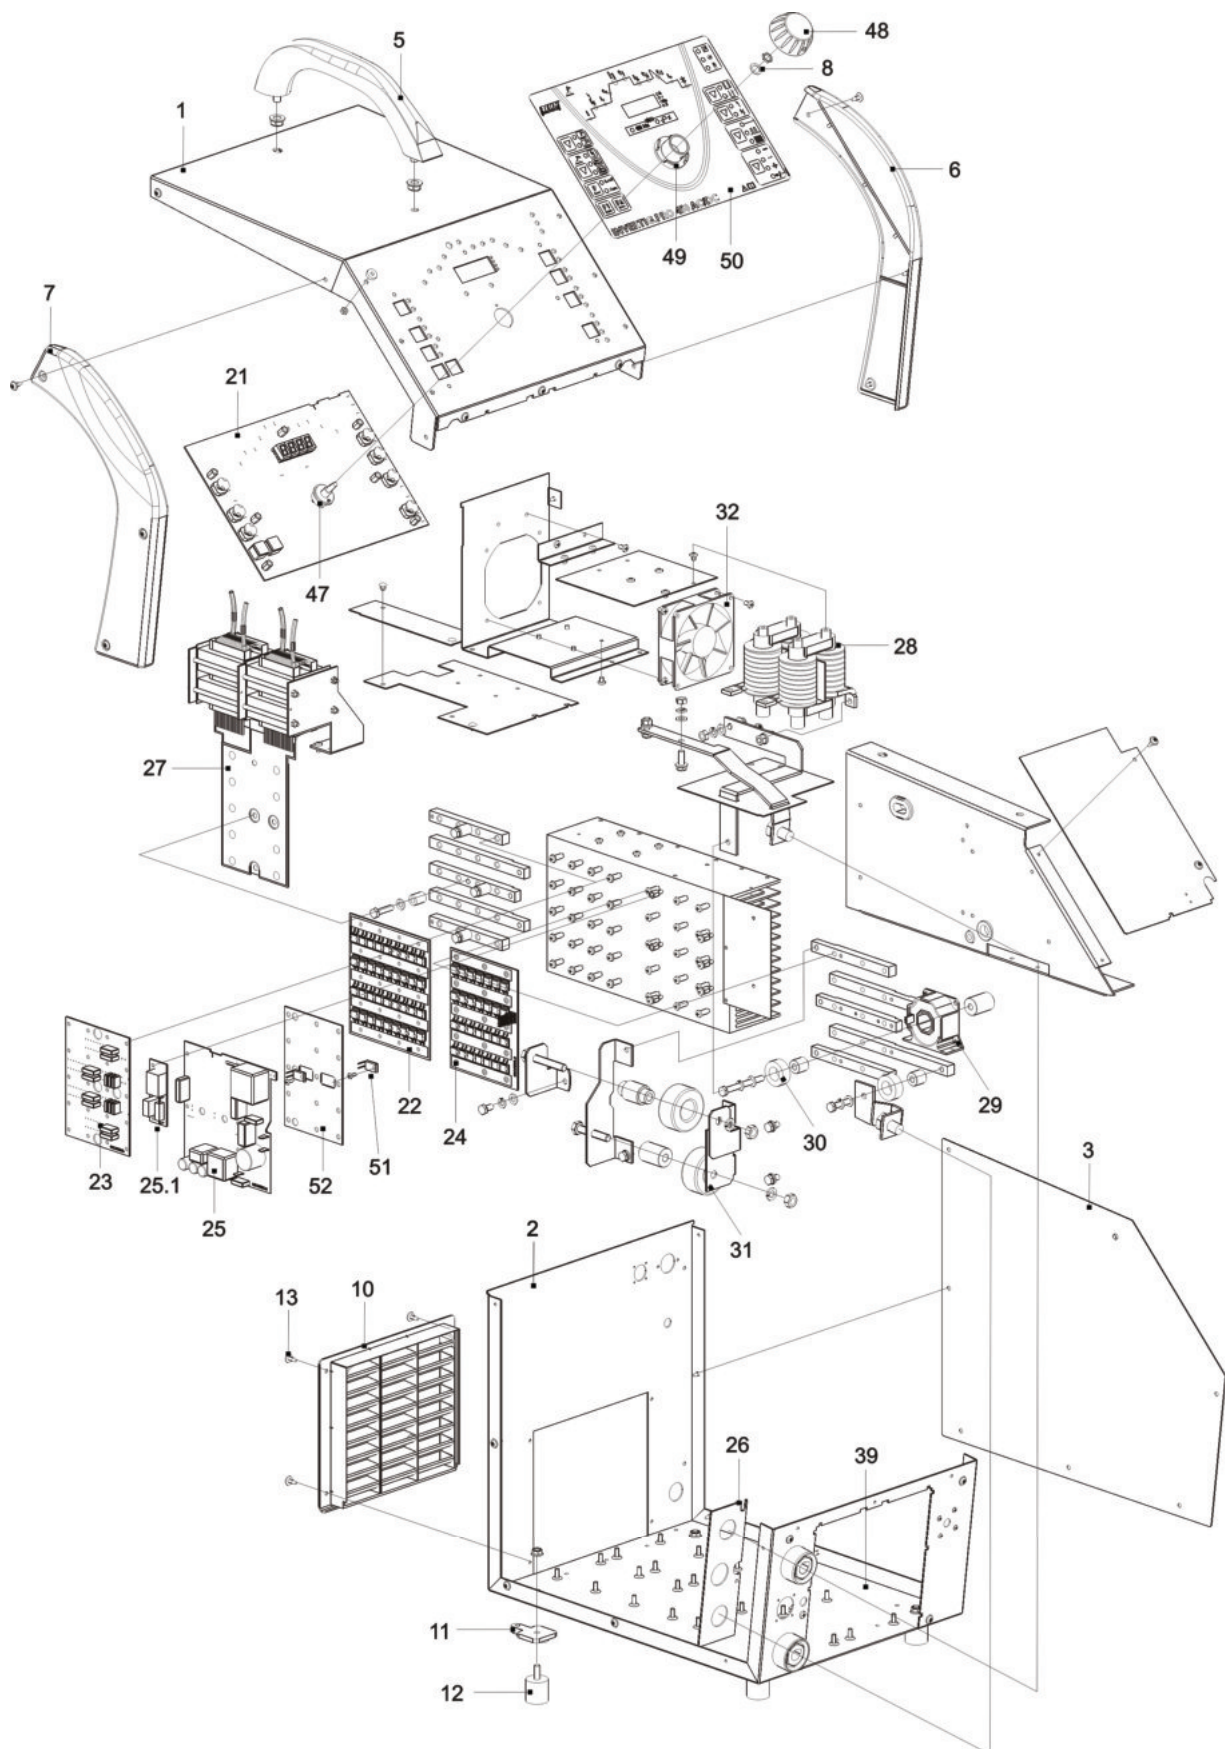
Explosionszeichnung INVERTIG.PRO 240 DC – 450 AC/DC (links)
